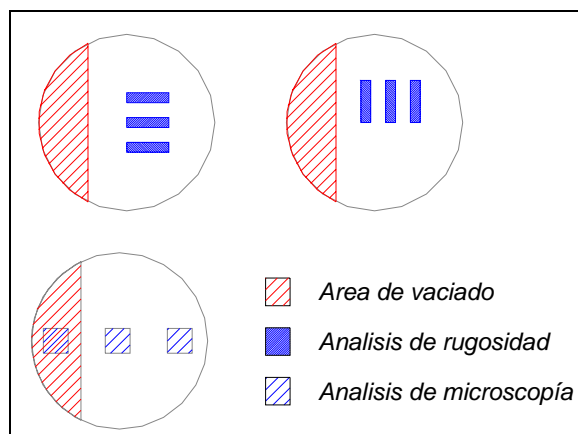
Esquema del arreglo del molde durante el vaciado. (Dimensiones en mm)
